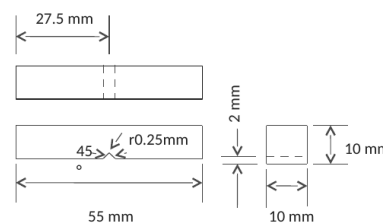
Dimensiones de las probetas de impacto Charpy según ASTM E-23 [9].
